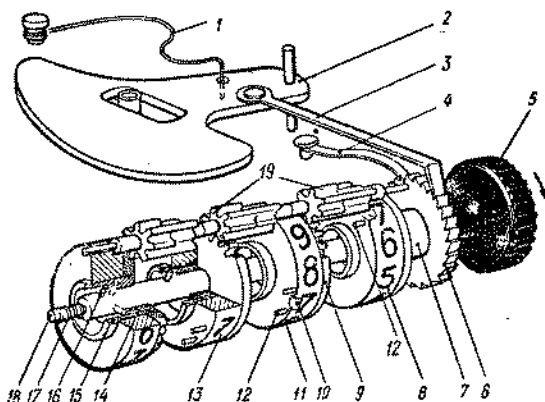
Кинематическая схема шагомера «Заря» ШМ-6:
